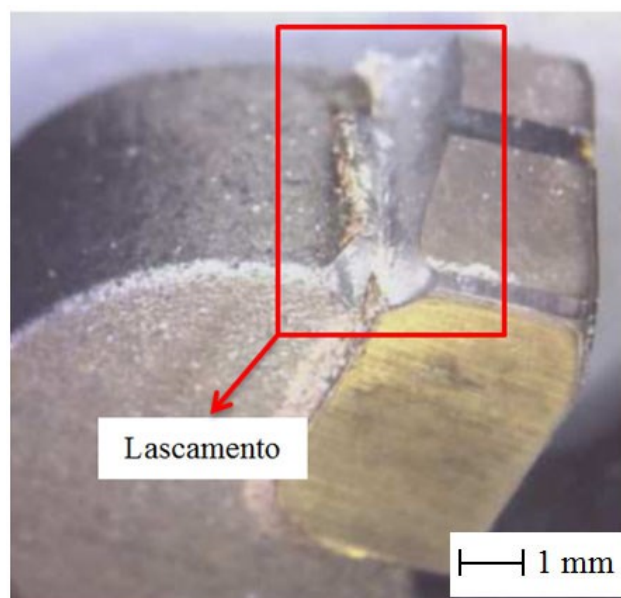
Desgaste do inserto de metal duro P20 após 100 cortes do tubo de aço S235JR
